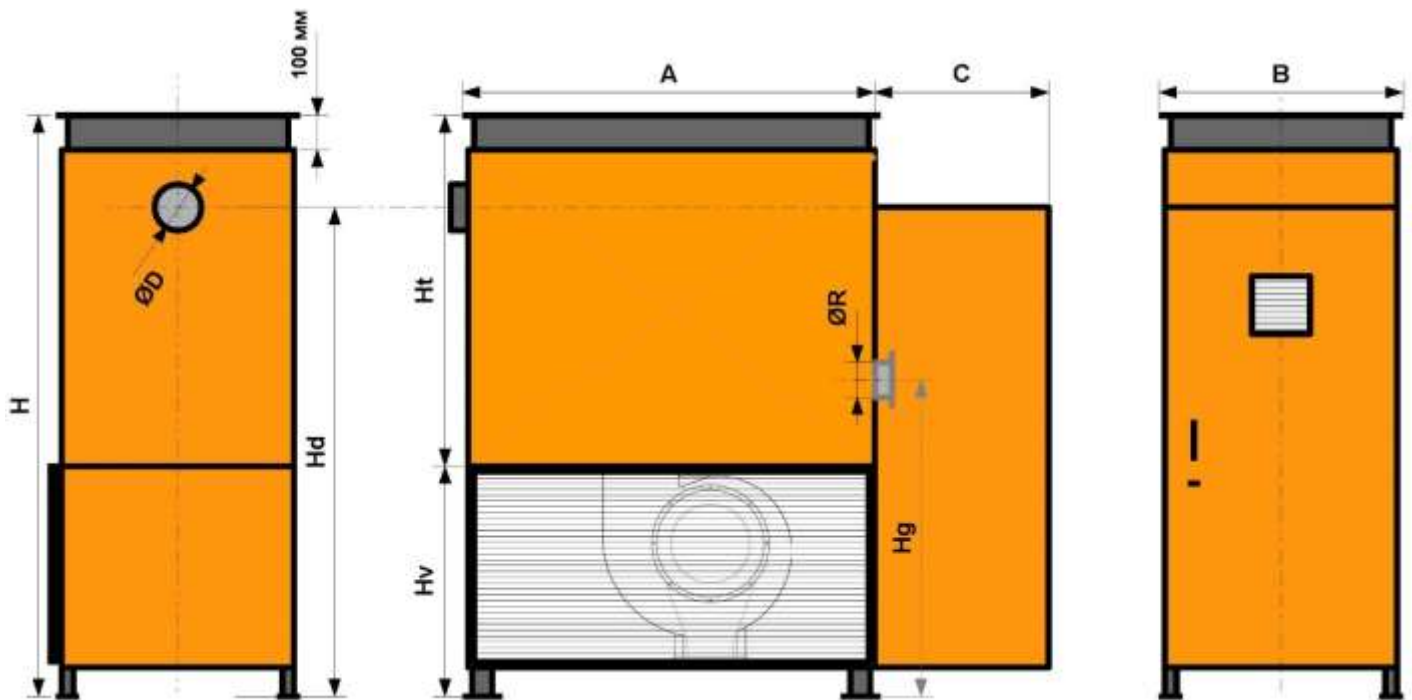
Габаритные размеры воздухонагревателей (теплообменников) серии VT-O
